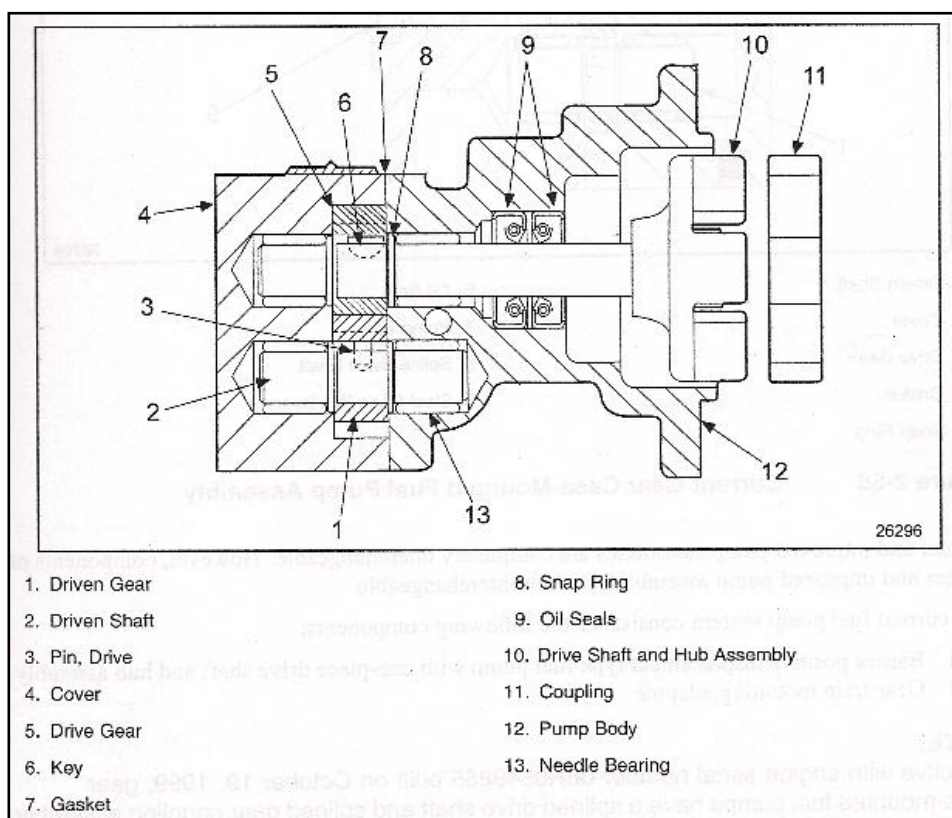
Partes de la Bomba de Combustible, Vista Lateral.⁶
